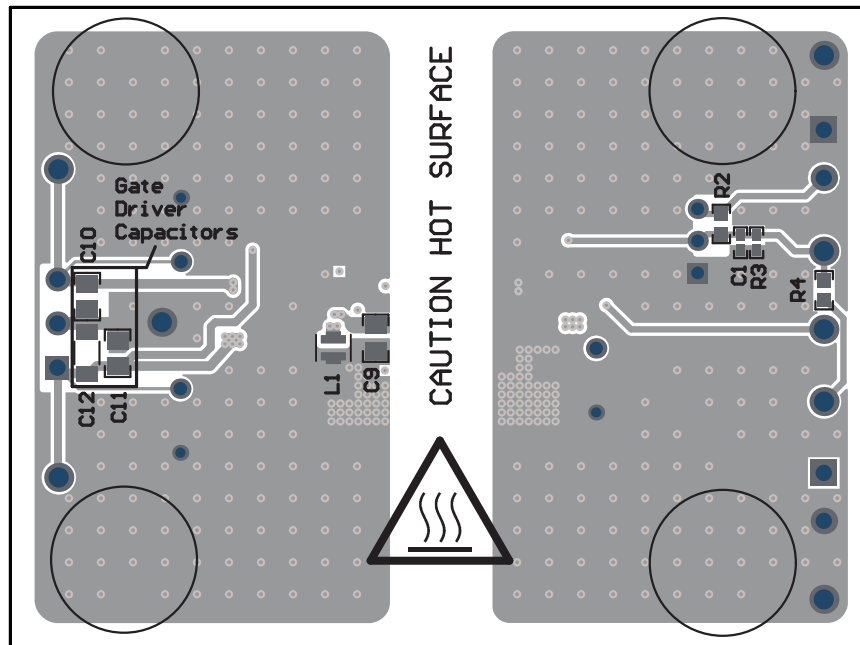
PCB の最下層、アセンブリ (ミラー図)
